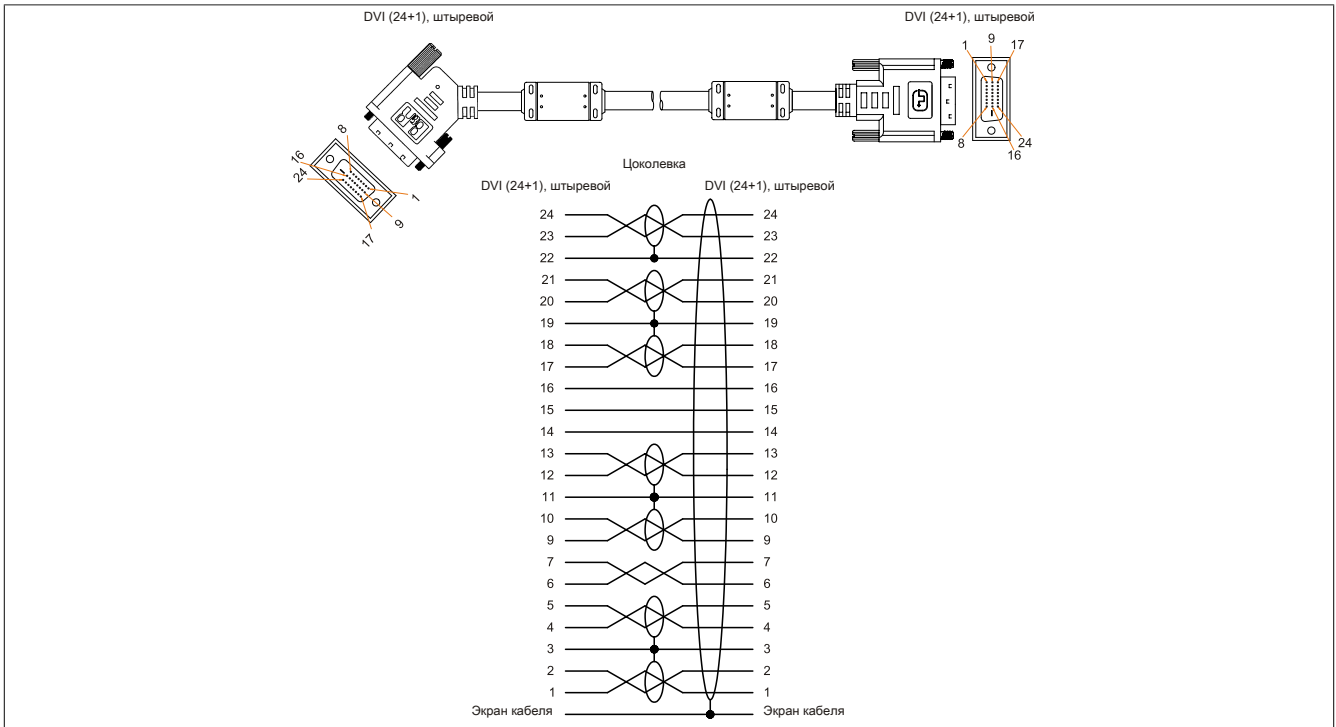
5CASDL.0xxx-01 — цоколевка
